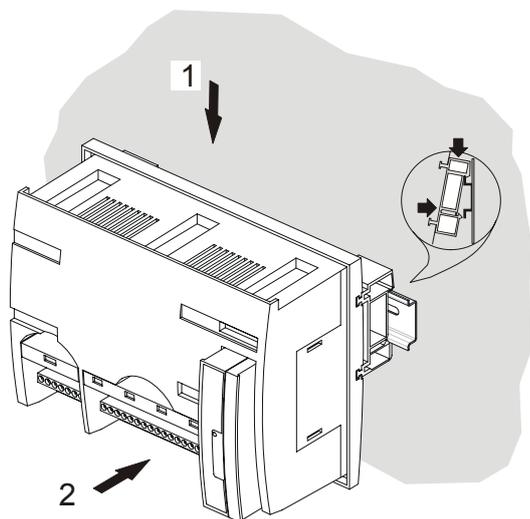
Установка контроллера с MMI внутри шкафа (б)
